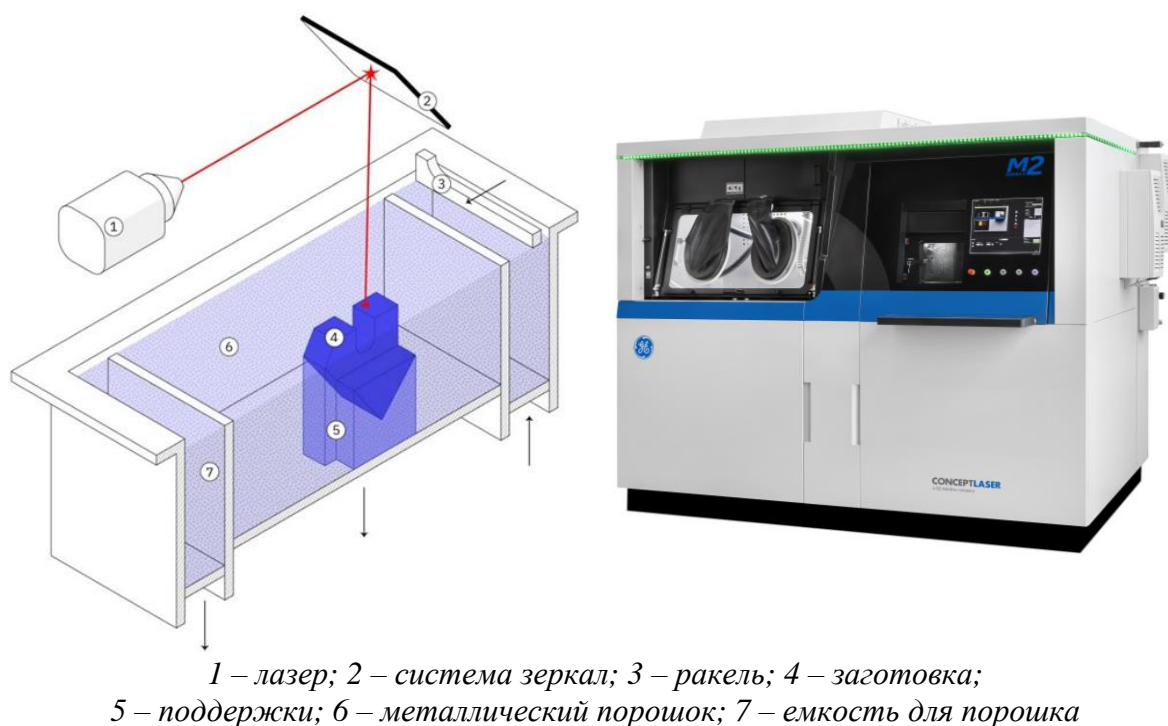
Схематичный процесс СЛС и внешний вид установки СЛС.
